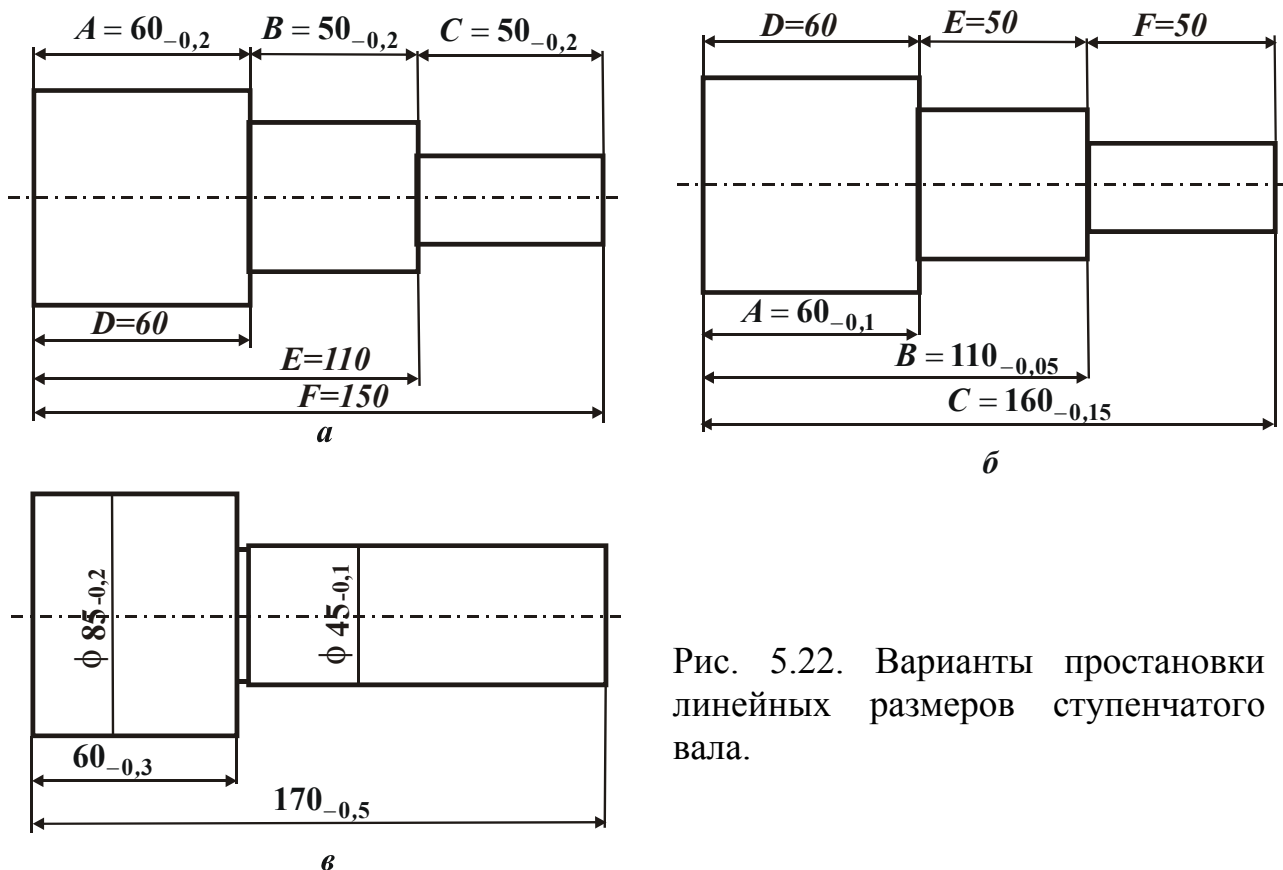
Варианты простановки линейных размеров ступенчатого вала.
